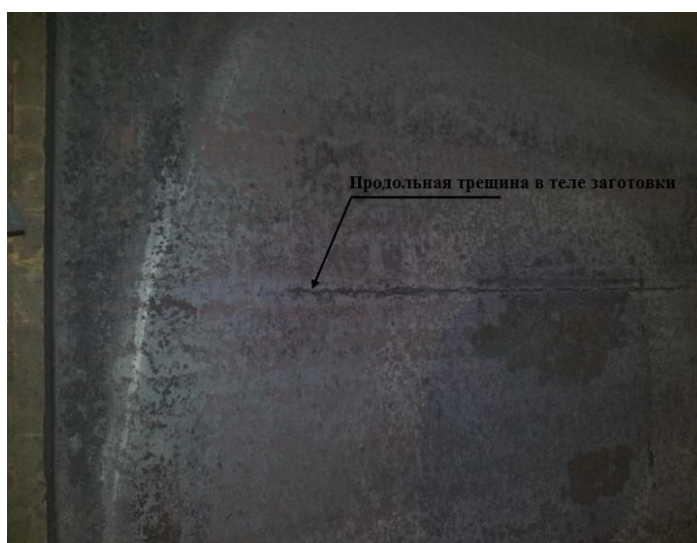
Продольная трещина в теле отливаемой заготовки
